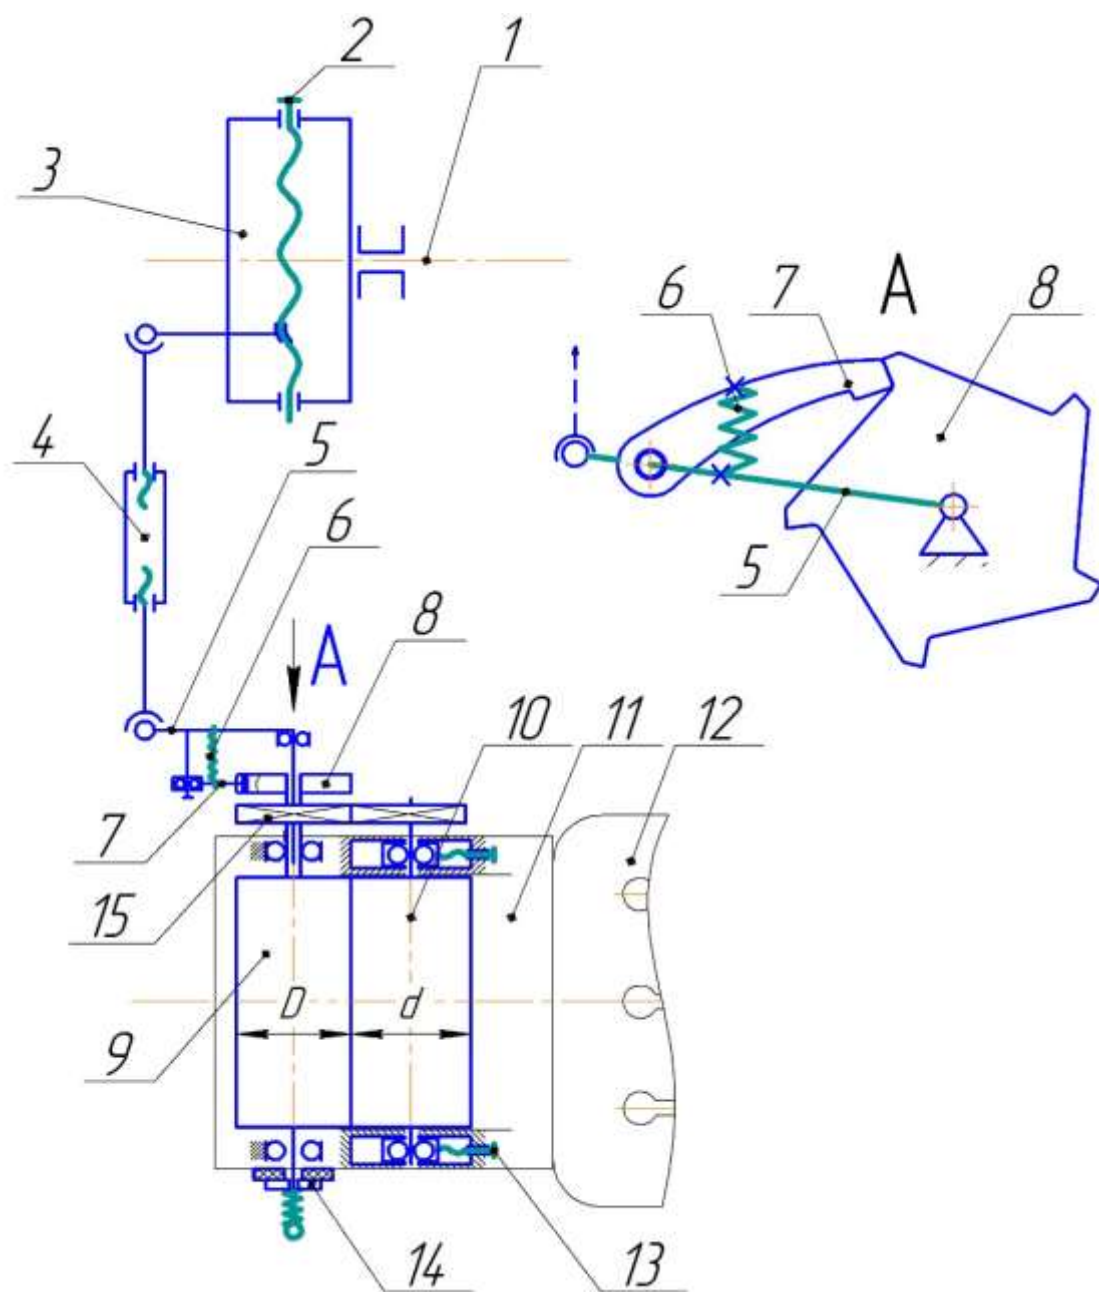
Кинематическая схема разрабатываемой валковой подачи
